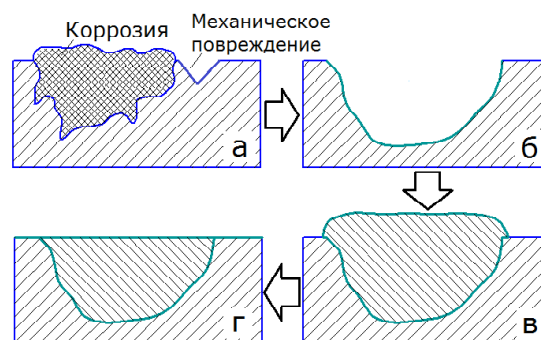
Схематическое изменение восстанавливаемых поверхностей: а – поверхность с дефектом; б – подготовка к напылению; в – напыление покрытия; г – поверхность после механической обработки
